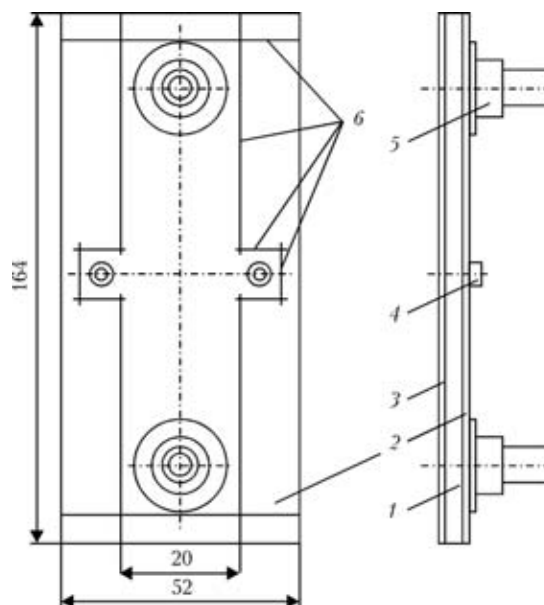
Схема измерительной камеры магнитопневматического газоанализатора типа ОХУМАТ: 1 — основание; 2 — верхняя пластина; 3 — нижняя пластина; 4 — ниппель; 5 — штенгель; 6 — нахлесточные сварные швы
